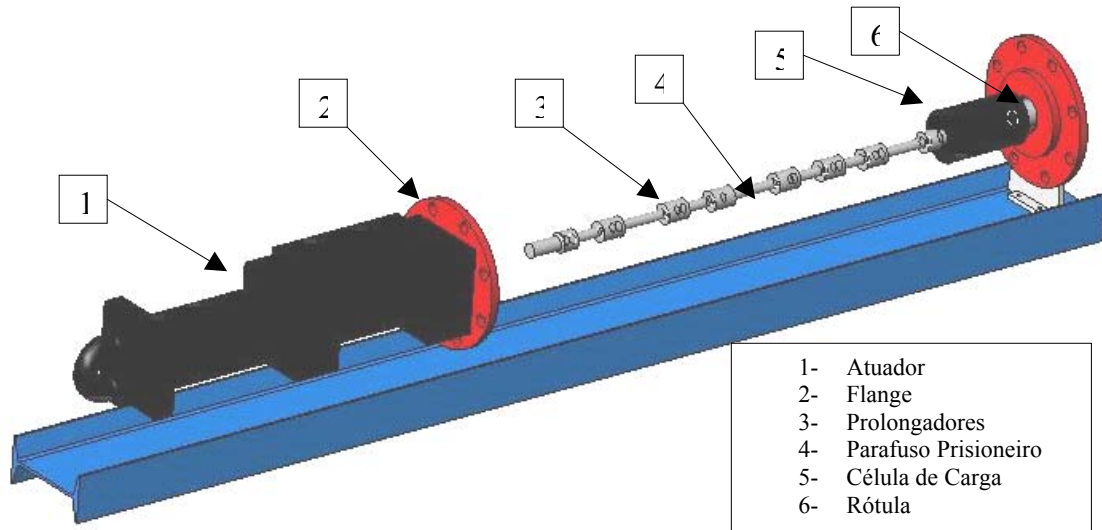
Esquema de montagem do dispositivo para ensaio de fadiga.
